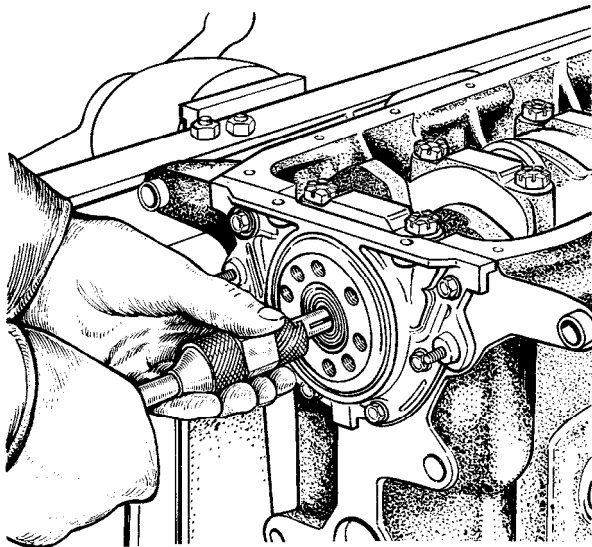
Выпрессовывание подшипника вала коробки передач из коленчатого вала выталкивателем А.40006
